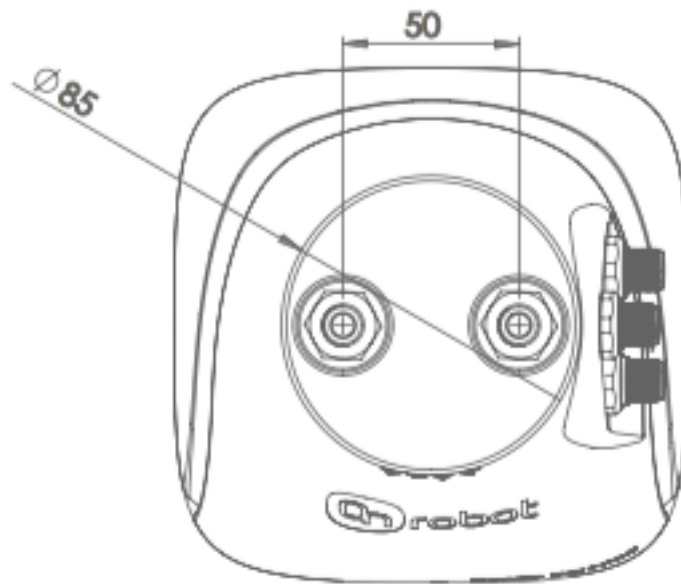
Dimensiones de la cara de montaje (superior) de Gecko Gripper.
